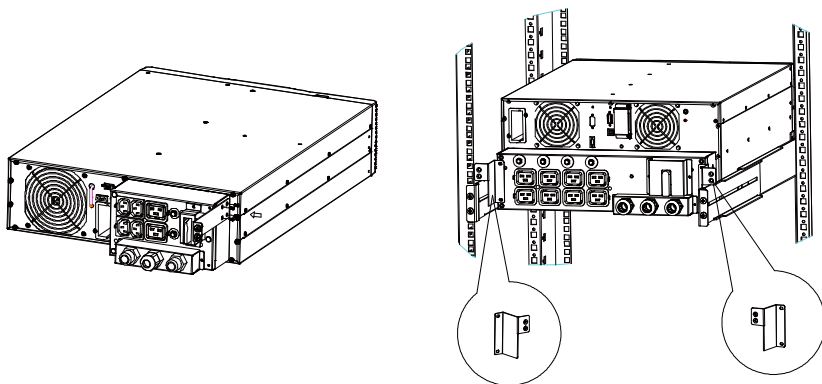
Installazione delle staffe del PDU sull'UPS
